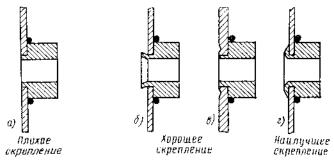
Скрепление деталей для предупреждения их смещения при пайке в печи:
